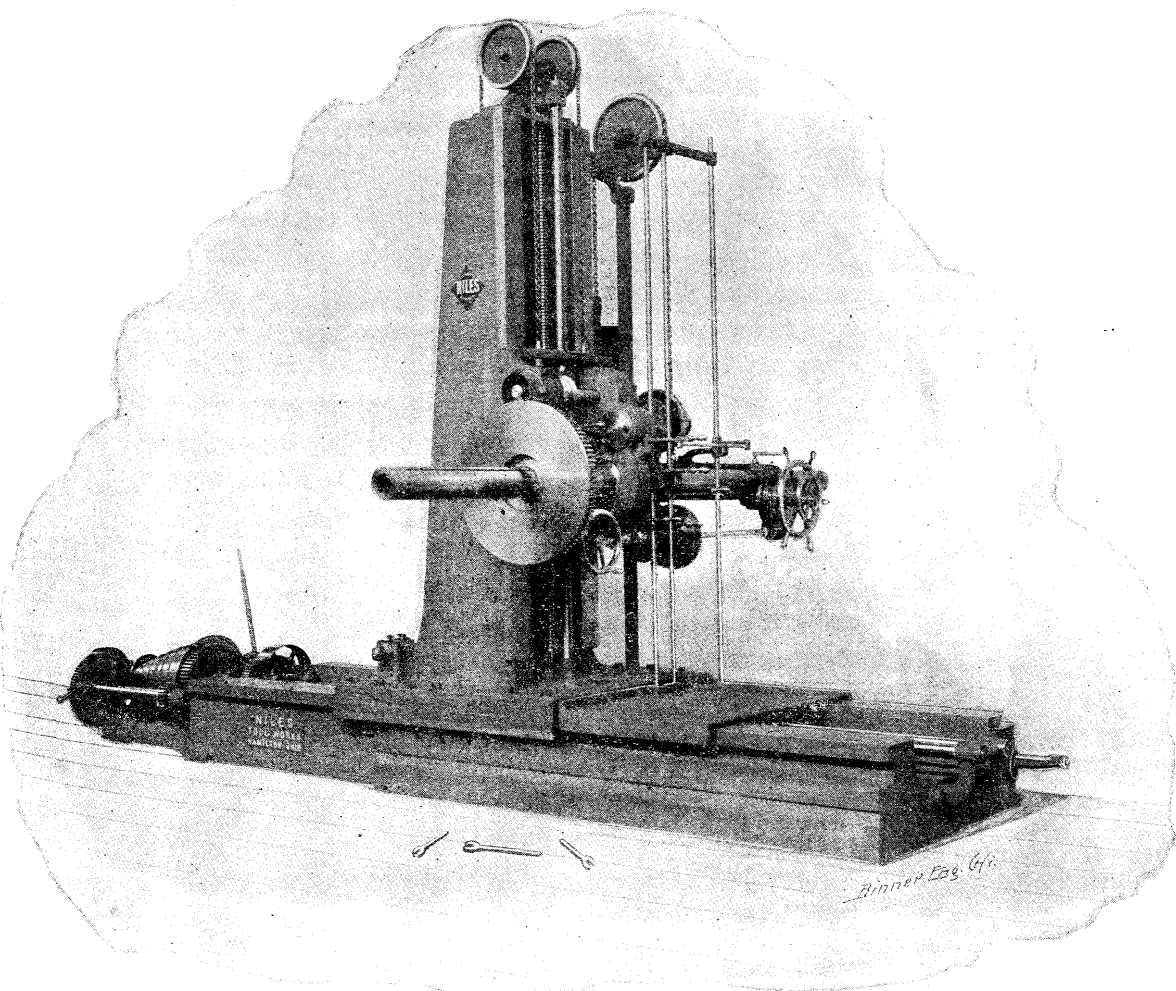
Fraiseuse-aléseuse-perceuse des Niles Tool Works; de Hamilton (E.-U.).
